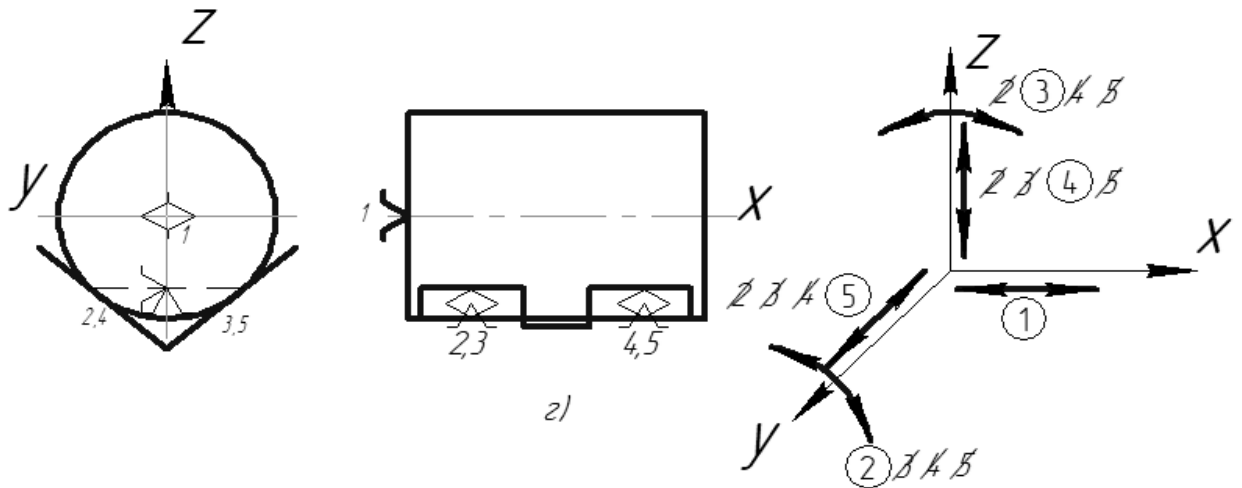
Базування циліндричної заготовки у призмах
